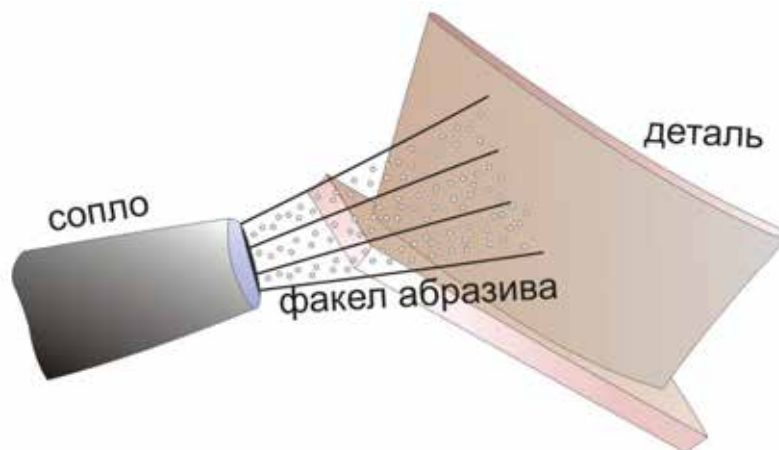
Схема струменево-абразивної обробки [12]
